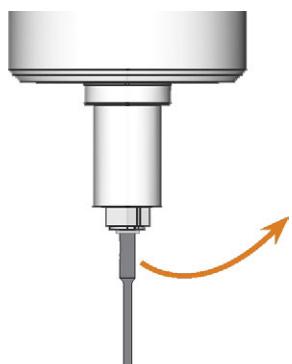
RIMOZIONE DELL'UTENSILE DALLA PINZA DI SERRAGGIO
